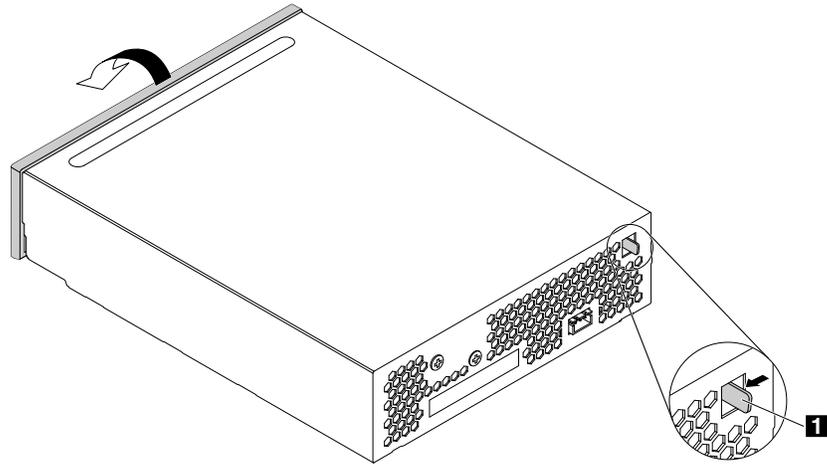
Ouverture du carter du boîtier de stockage d'accès frontal
